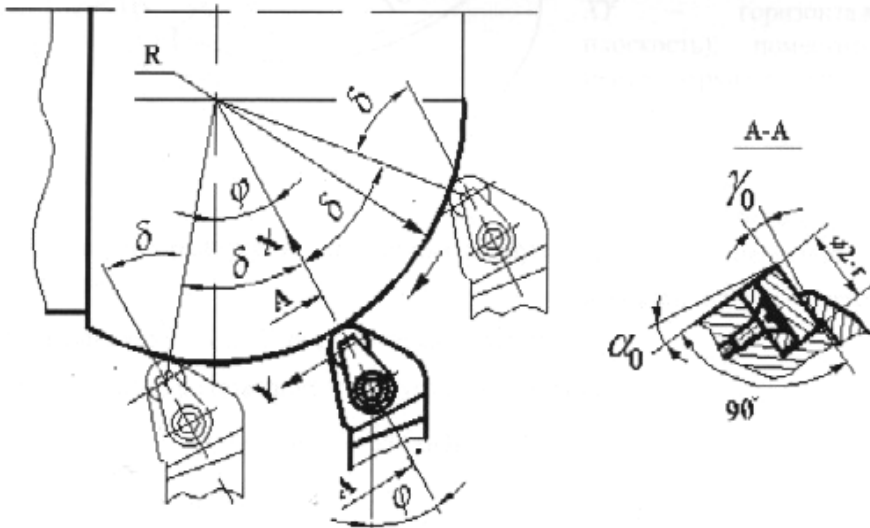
Схема для определения положения вершины резца на контурной линии детали
